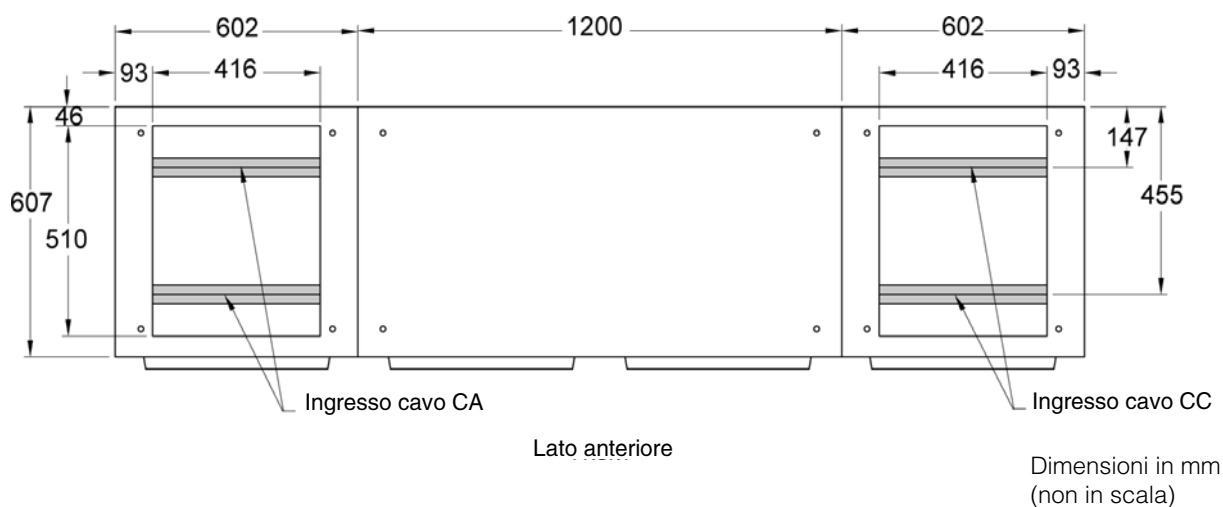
Ingressi tubo protettivo armadio, vista dall'alto
